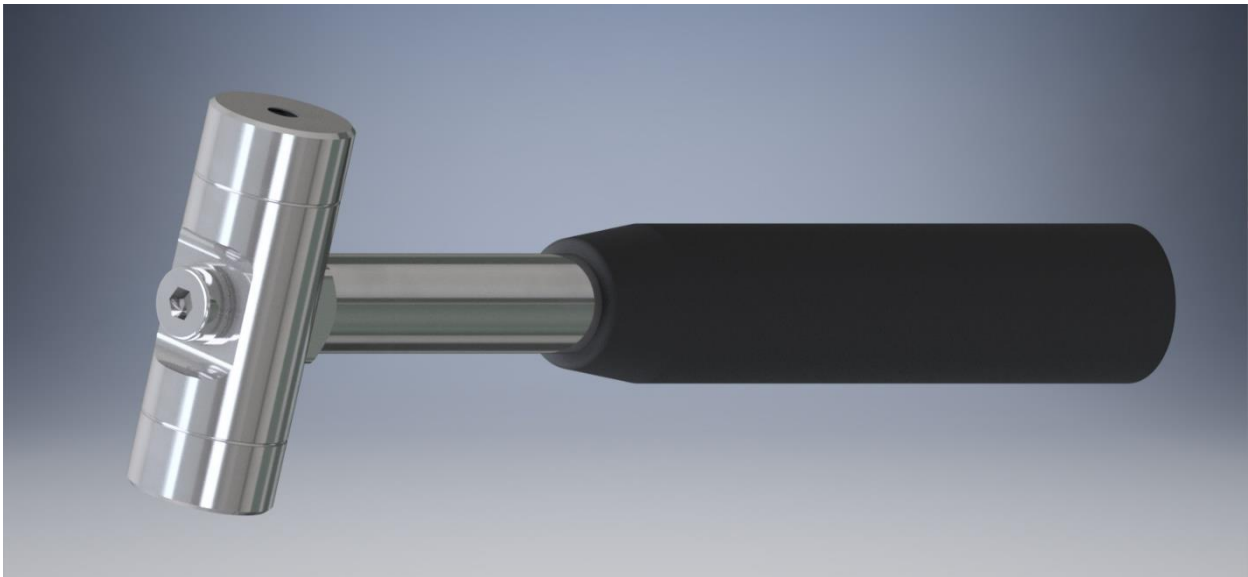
Impulse hammer, ensamble modelado mediante Autodesk Inventor.
